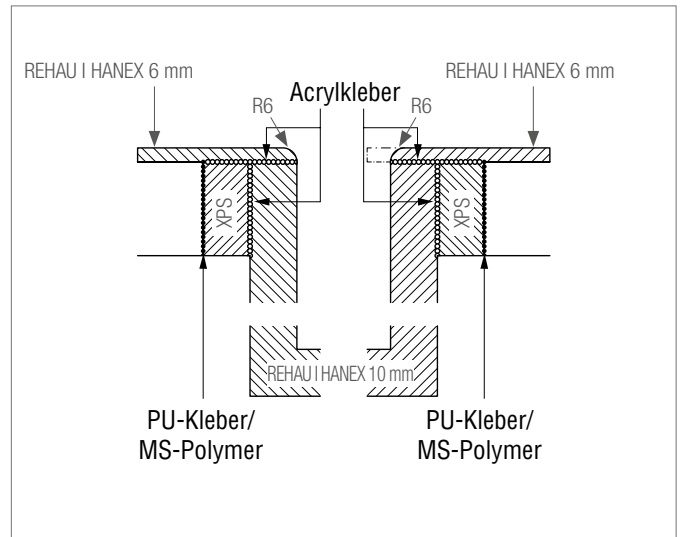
Ausschnittskanten bündig fräsen und mit Radius versehen
